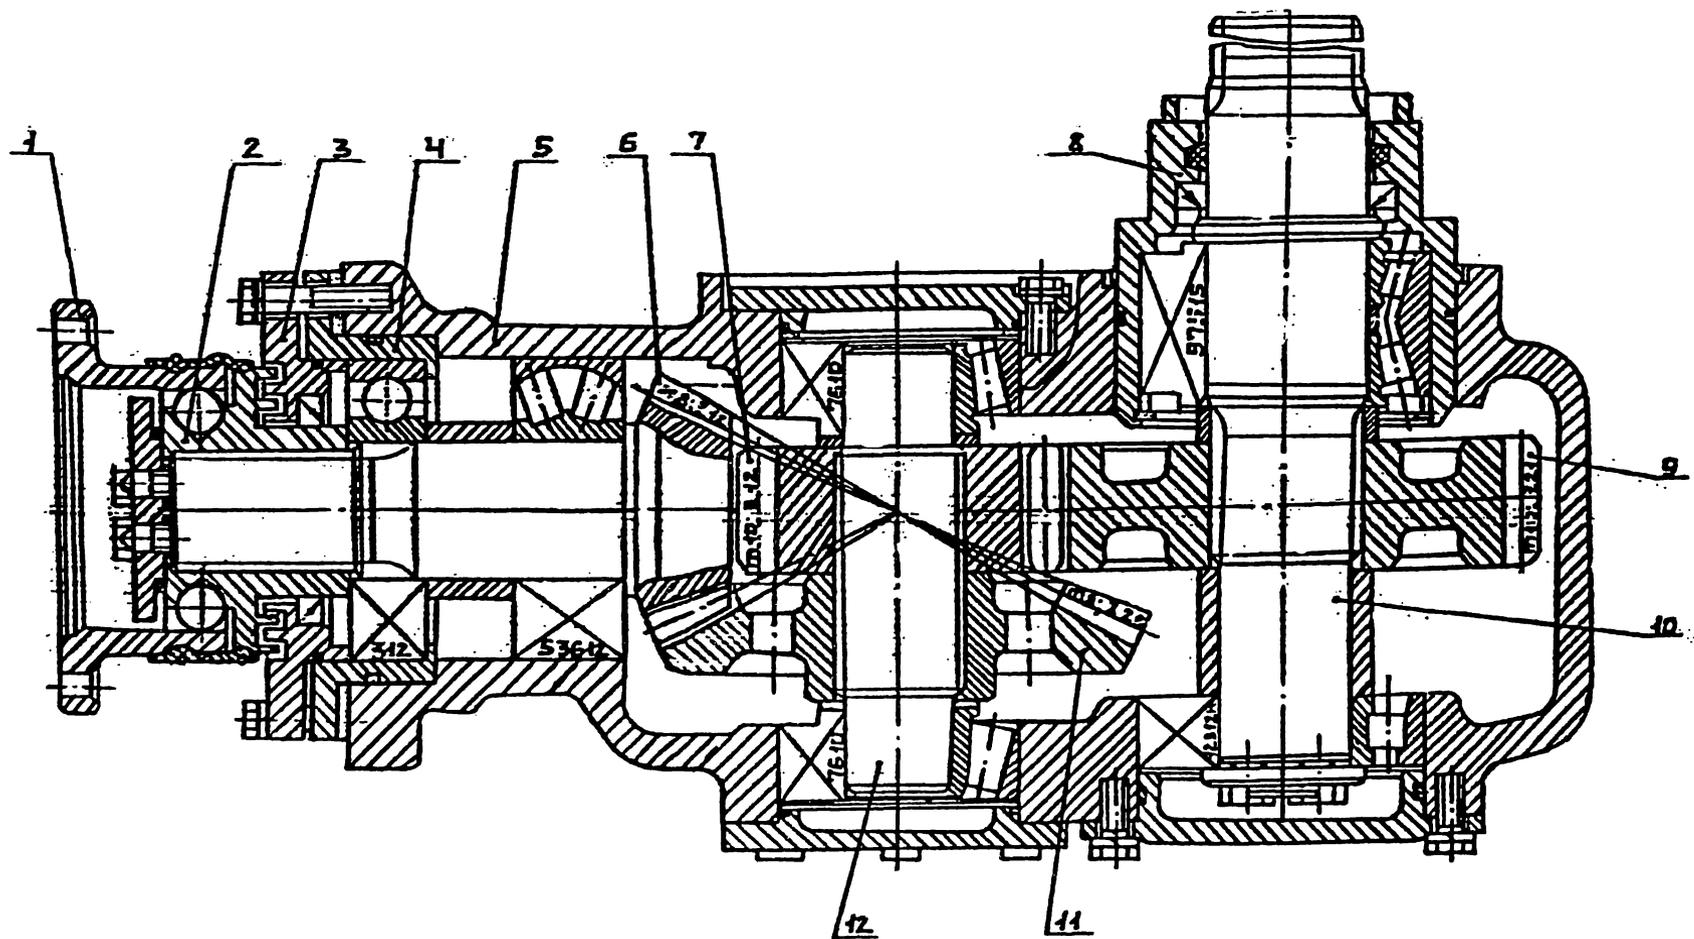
Редуктор конический конвейера комбайна «Урал-20Р» :
